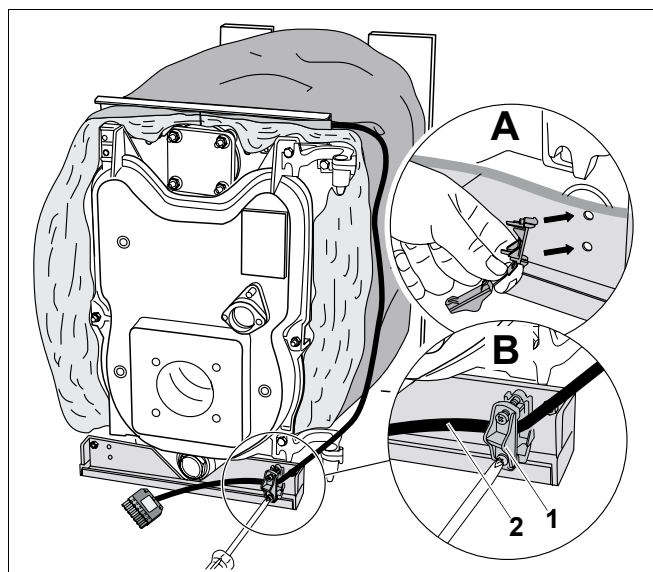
Установка фиксатора провода и прокладка кабеля горелки
